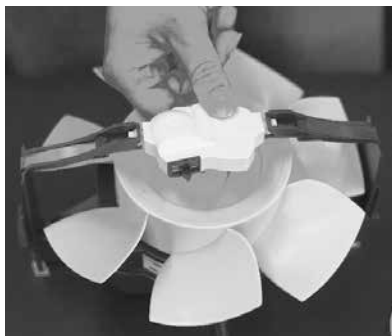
Tourner l'engrenage à 90 degrés ...
